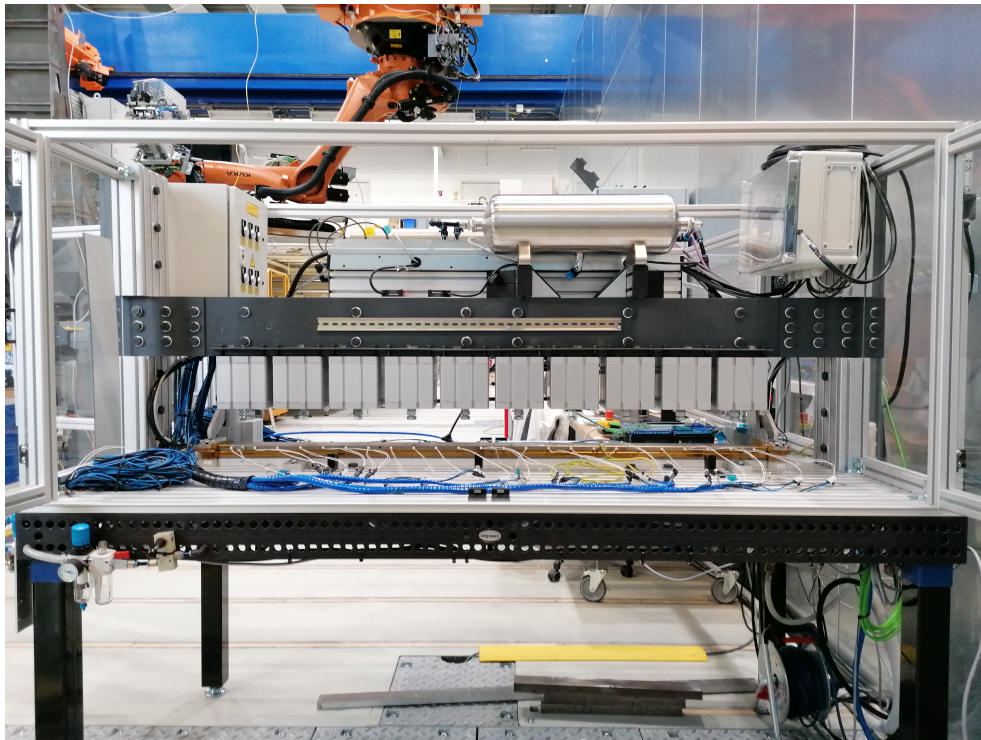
Schweißanlage zum elektrischen Widerstandsschweißen
